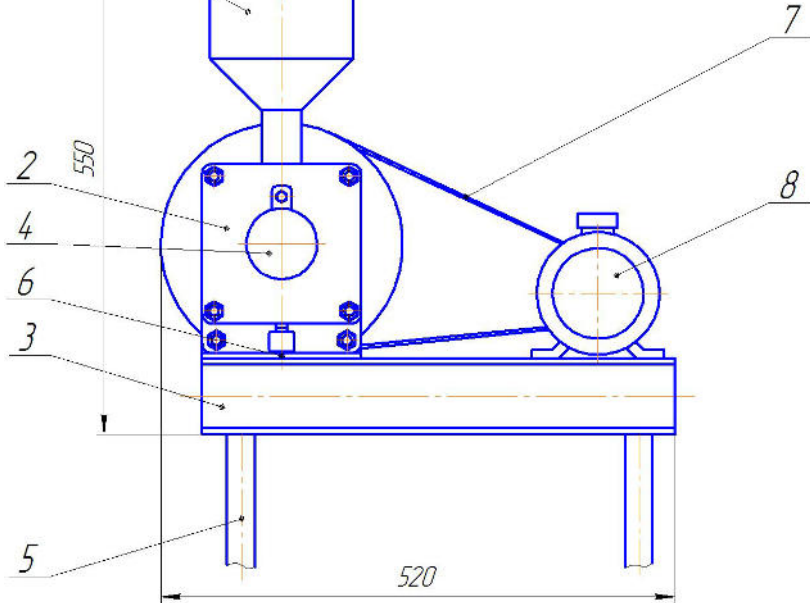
Устройства для подачи металлического порошка в горелку
